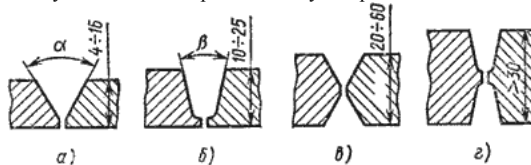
Формы подготовки кромок под сварку:
